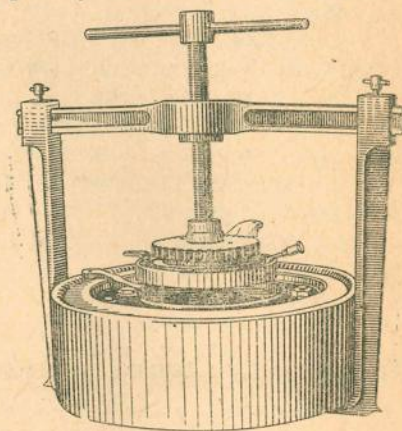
Запрессовка ведущего вала бортового фрикциона при помощи приспособления
